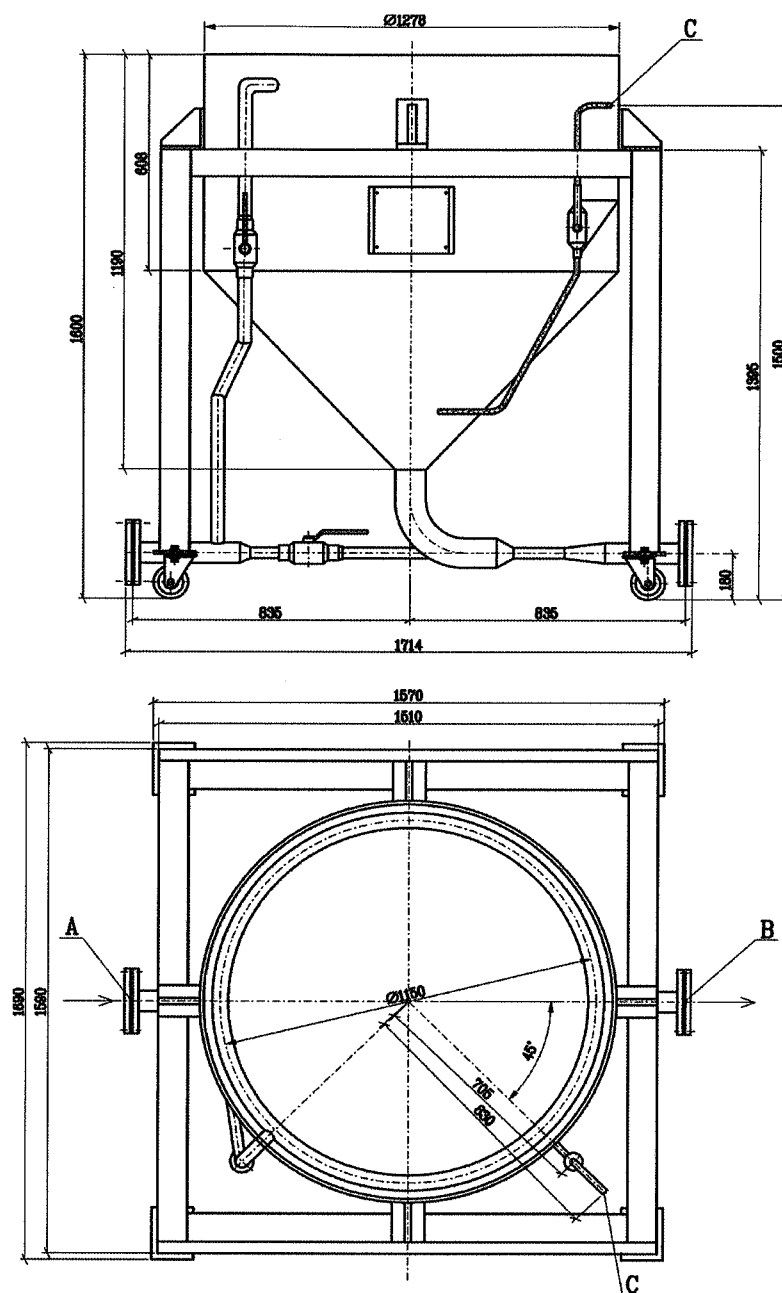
Габаритный чертеж гидротранспортера LCQ01AF001
